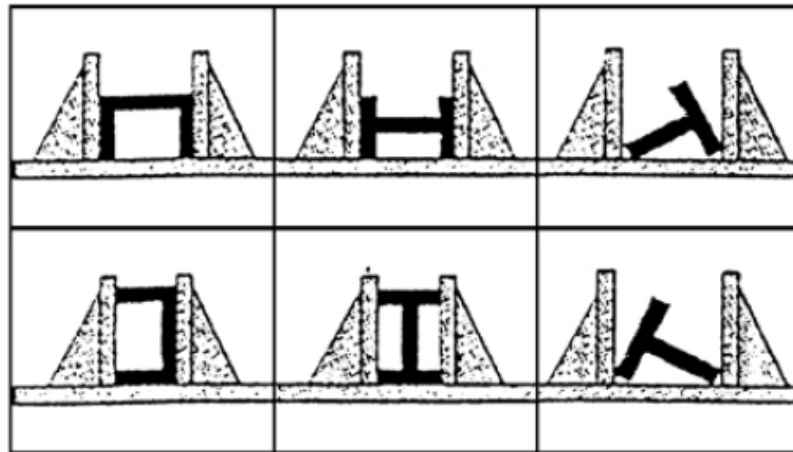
Рекомендуемые способы укладки металлопроката в тиски станка
